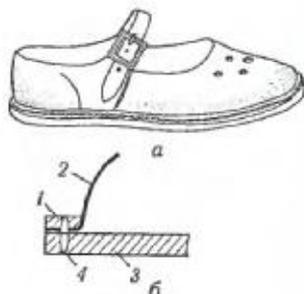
Сандальне кріплення: *a* — зовнішній вигляд; *b* — схема кріплення; 1 — рант; 2 — заготівка; 3 — підшва; 4 — нитковий шов
